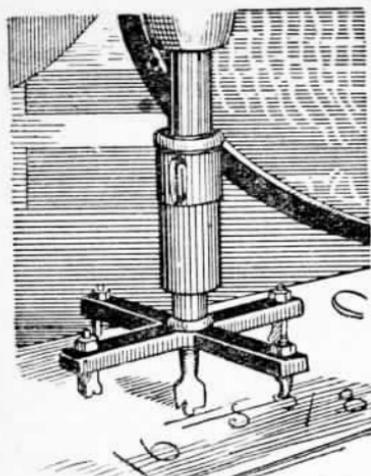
а. Машинка для высверливания кольцевых дорожек.
